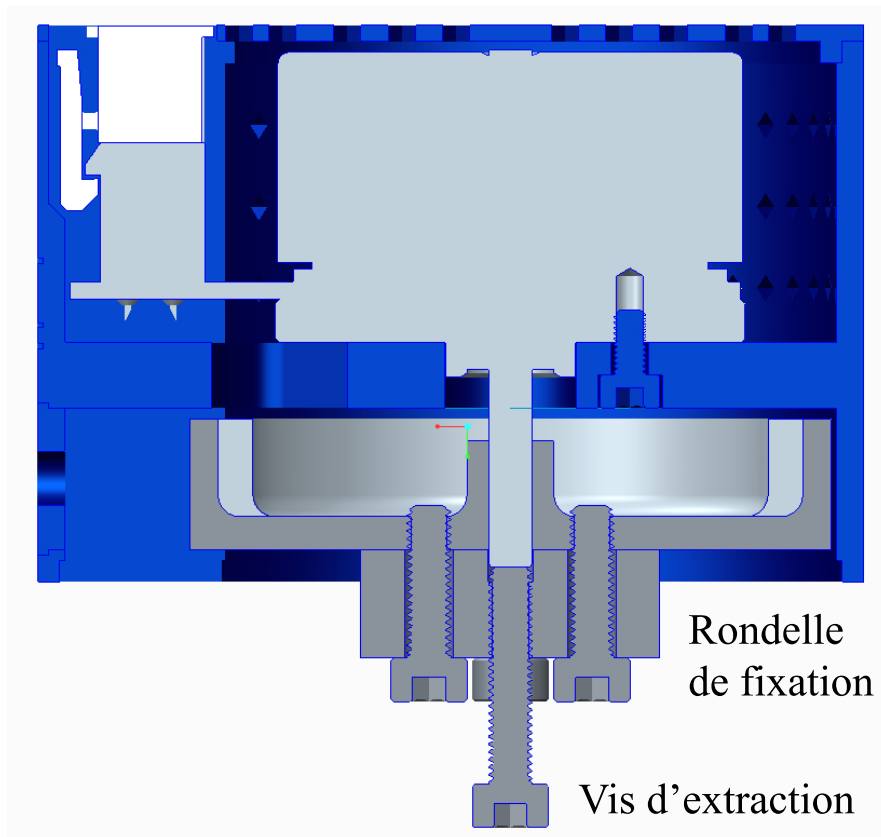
Vue de coupe de l’extracteur à vis. Cette assemblage est utilisé pour le démontage du joint collé entre l’arbre du moteur et l’ajustement coulissant de la roue d’inertie.
